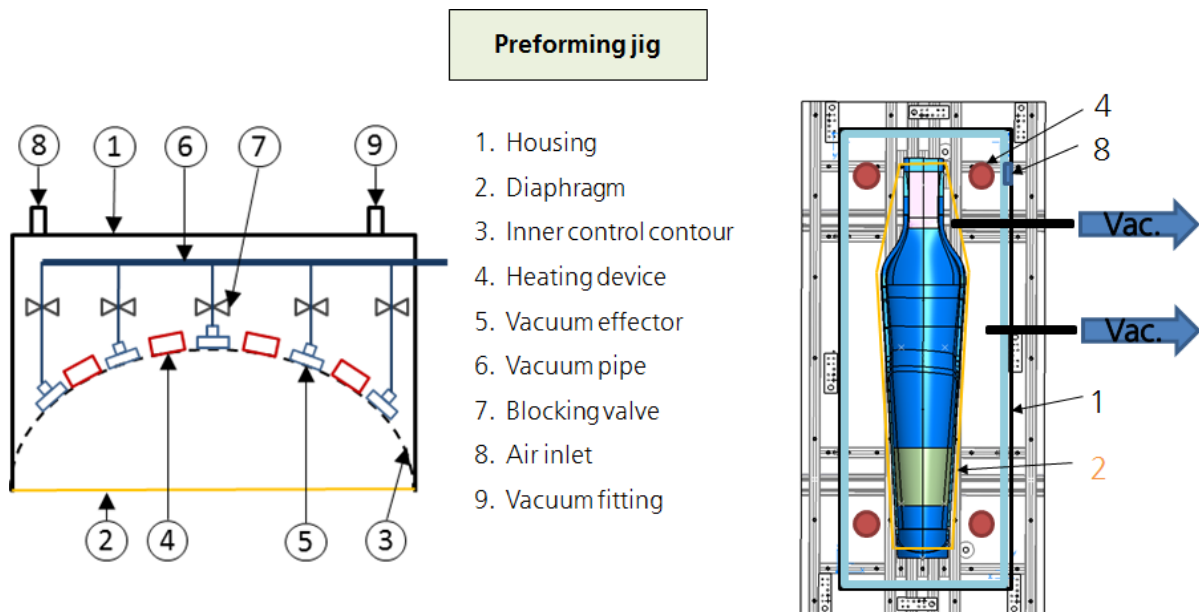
Steuerbare Preformeinrichtung (links: Querschnitt, rechts: Draufsicht)
